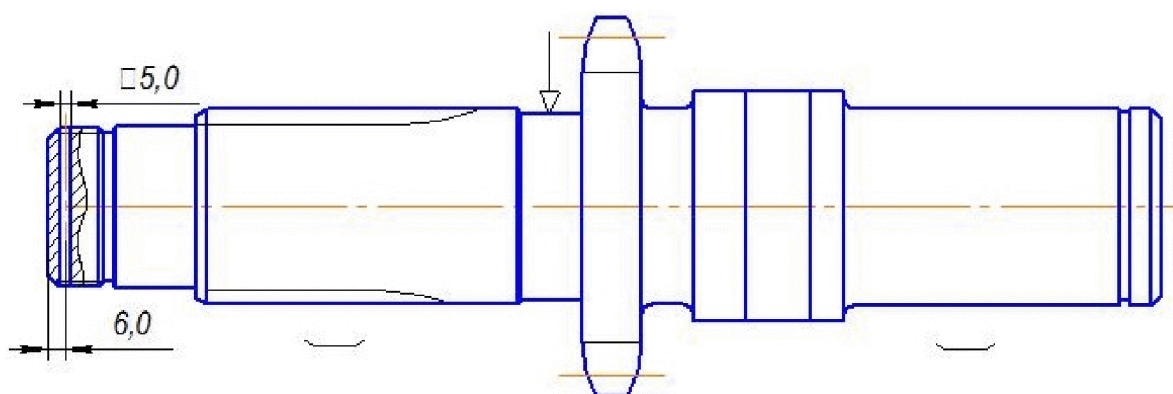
Базування, закріплення заготовки і поверхня, що обробляються
